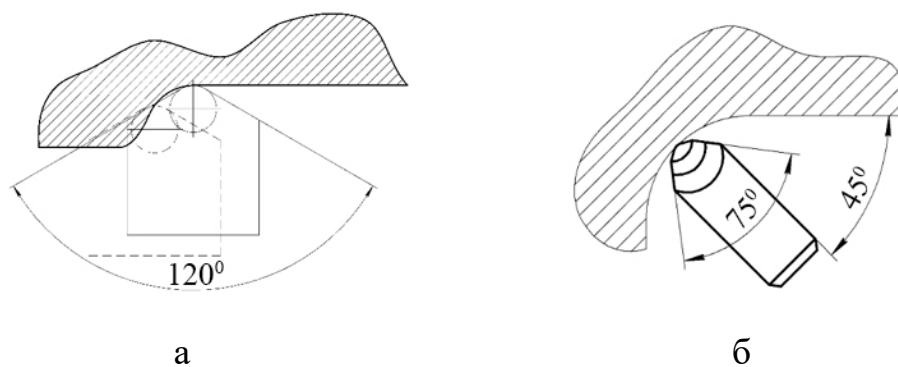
Положення стандартного вигладжувача при обробці конструктивного концентратора напружень типу «Поверхня поєднання двох діаметрів»: а – при використанні стандартного вигладжувача; б – при використанні модифікованого вигладжувача
